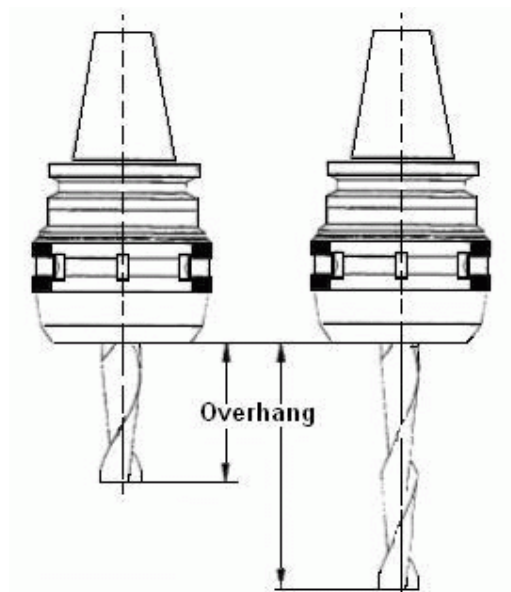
comprimento da ferramenta externo a fixação (overhang)
